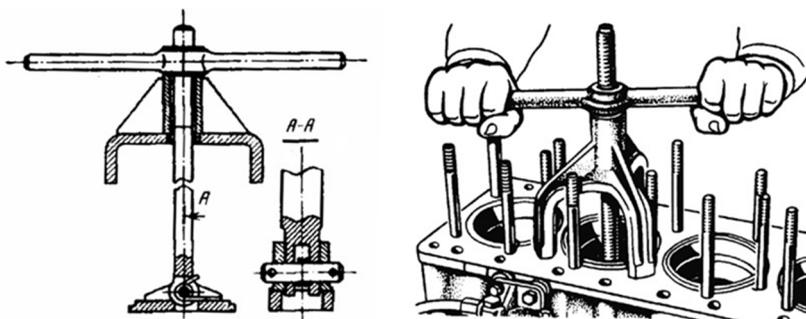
Схемы и существующие приспособления для выпрессовки и запрессовки гильз цилиндров
